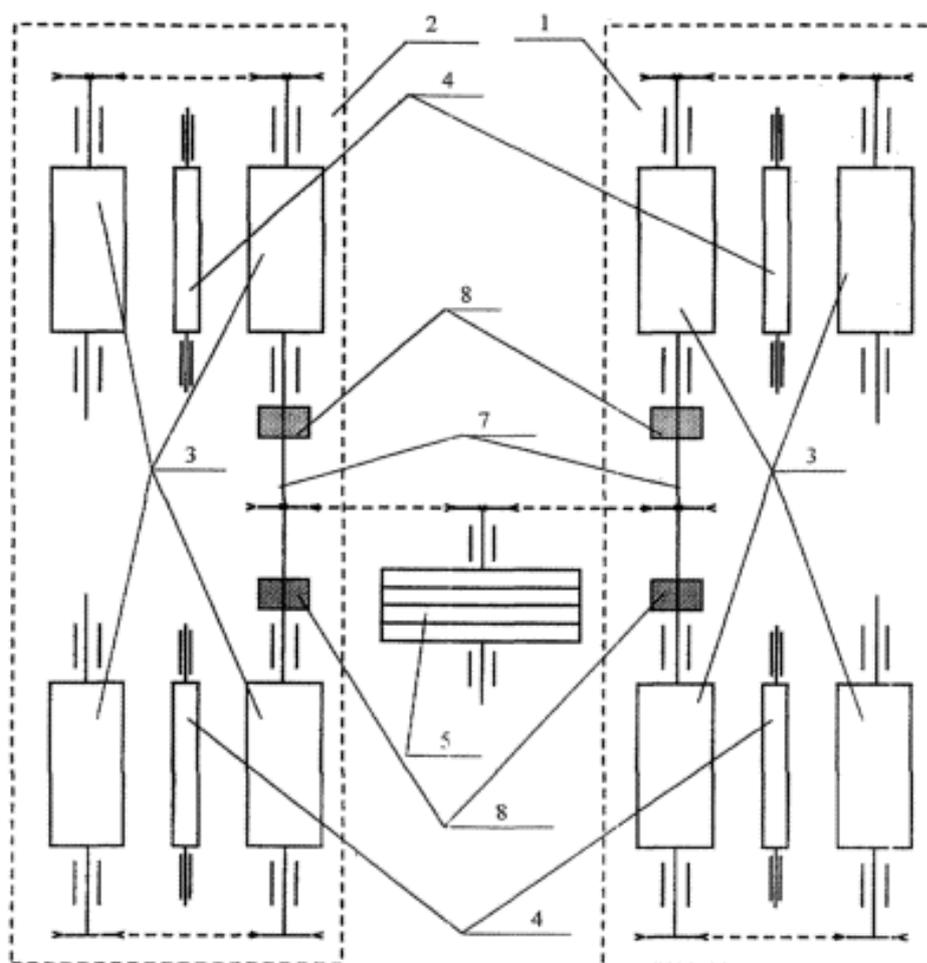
Схема тормозного стенда кинематического типа.
